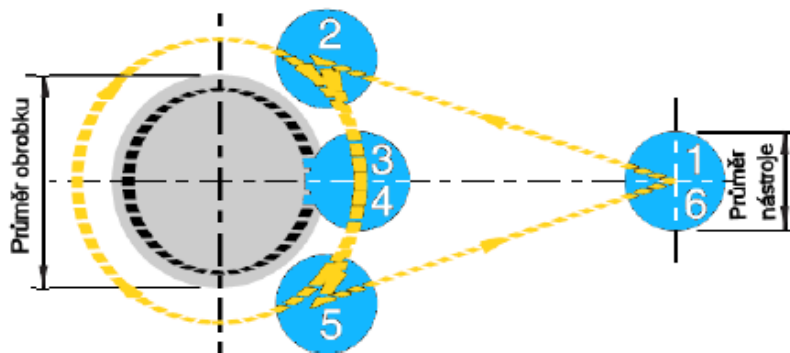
Principy pohybu pro frézování vnějšího závitu.[7]
